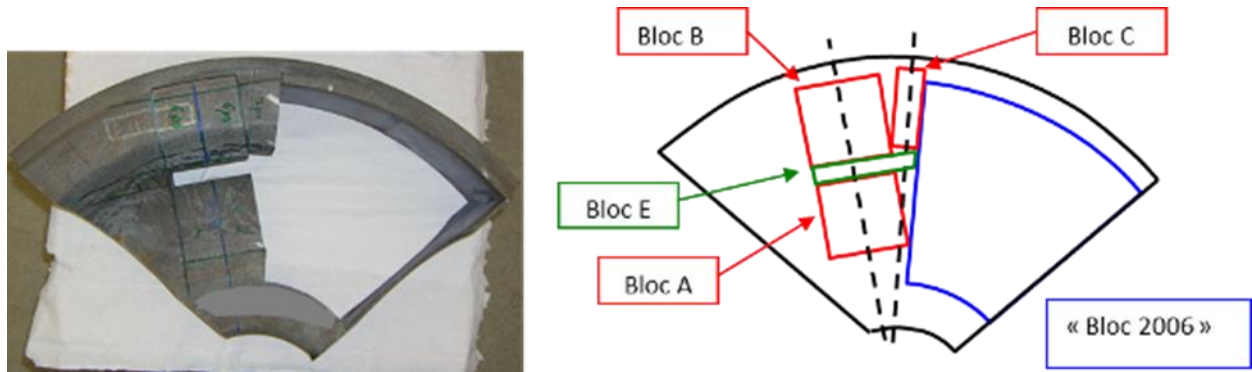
Schéma de prélèvement des éprouvettes à section carrée
